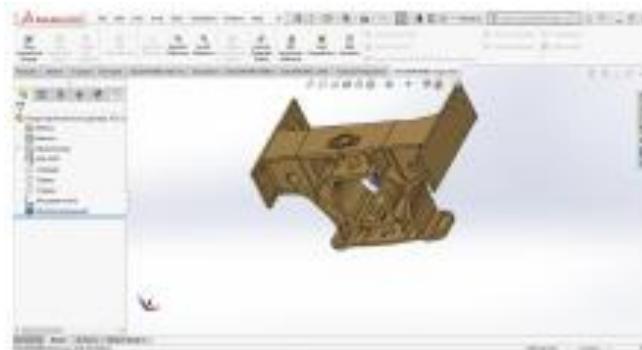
Опора вертикального шарніра в середовищі SolidWorks
